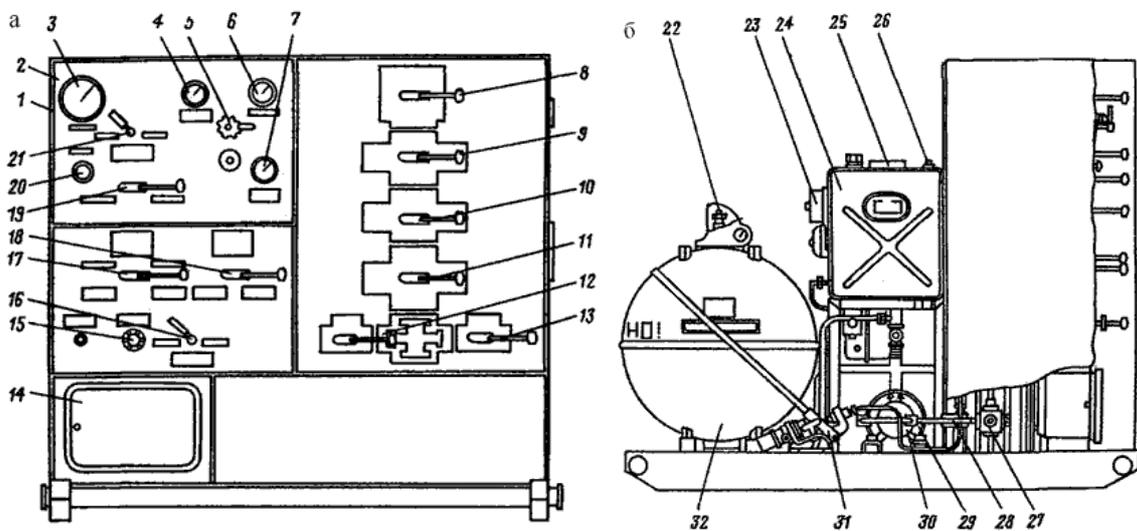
Общий вид станции гидроуправления ГУП-14 с основным пультом: а – вид спереди; б – вид сбоку; 1 – корпус; 2 – панель приборов; 3, 4, 6, 7 – манометры; 5 – клапан редукционный; 8–13; 17–19 – рукоятки управления; 14 – электрооборудование; 15 – вентиль; 16, 21 – блок кранов; 20 – выключатель; 22 – вентиль; 23 – звонок громкого боя; 24 – бак масляный; 25 – заливная горловина; 26 – щуп; 27 – клапан предохранительный; 28 – обратный клапан; 29 – электродвигатель; 30 – насос аксиально-поршневой; 31 – насос ручной; 32 – пневмогидроаккумулятор
